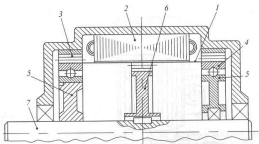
Мотор-редуктор на основе волнового механизма [56]:
